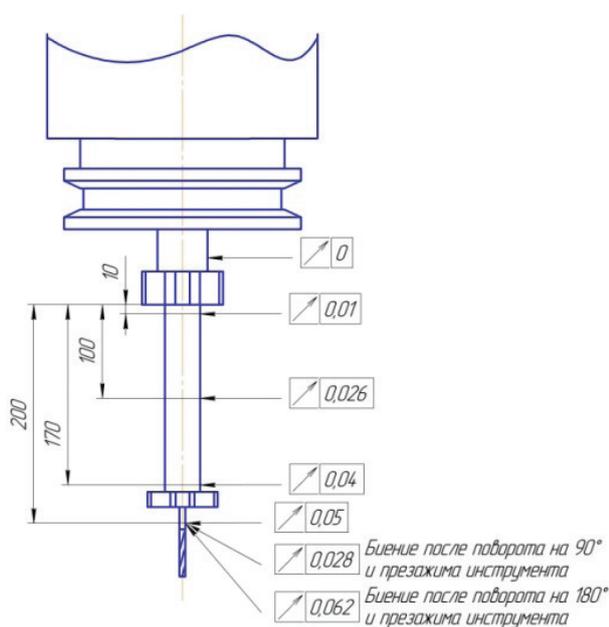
Схема измерения биения удлинительной оправки и фрезы, установленной в шпинделе станка для обработки радиусных канавок пресс-форм РТИ
